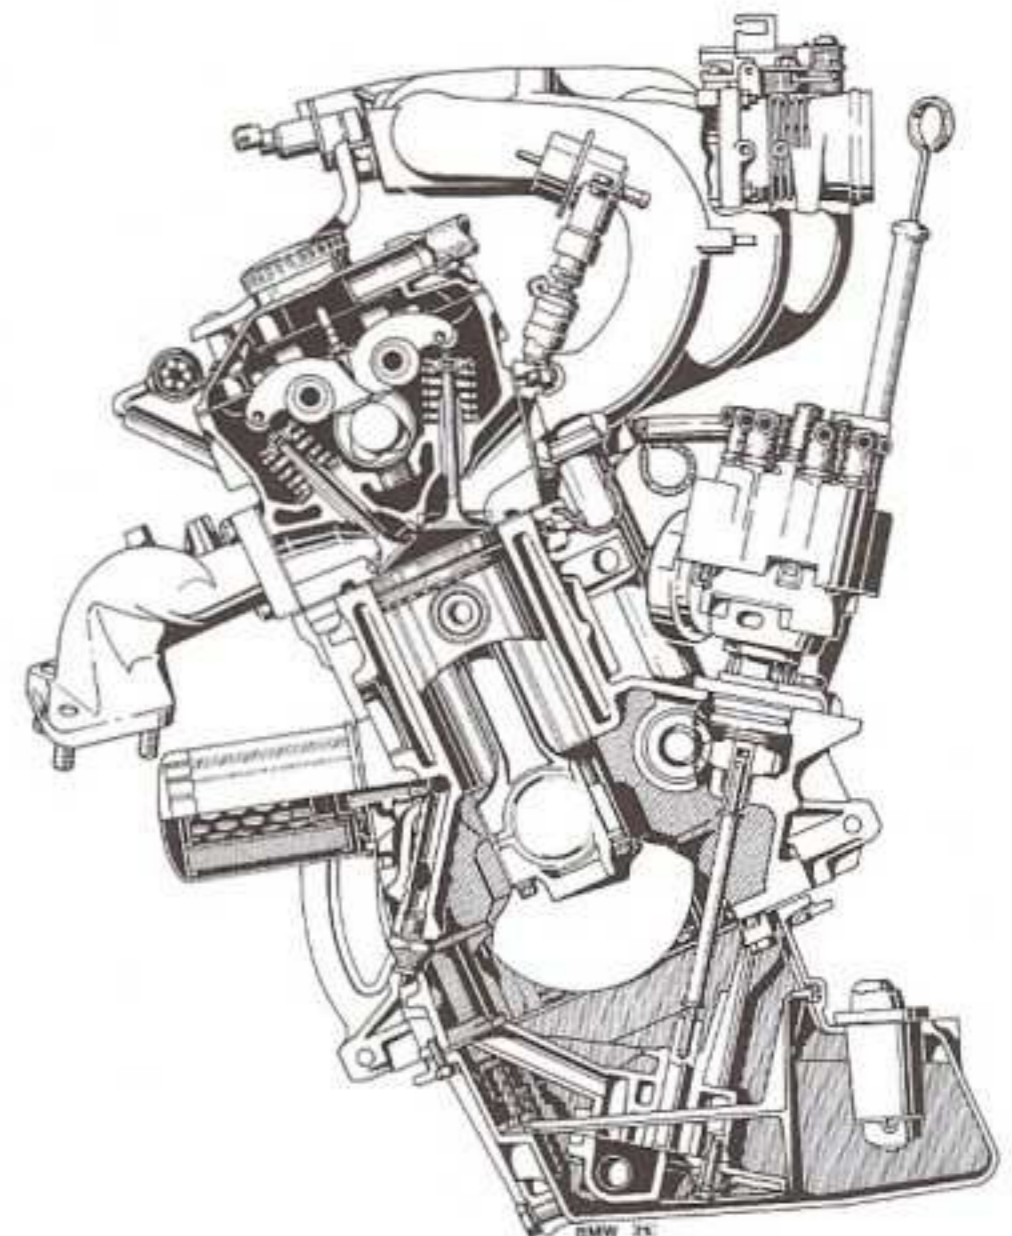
Schrägansicht des Sechszylinder-Einspritzmotors des BMW 320i
